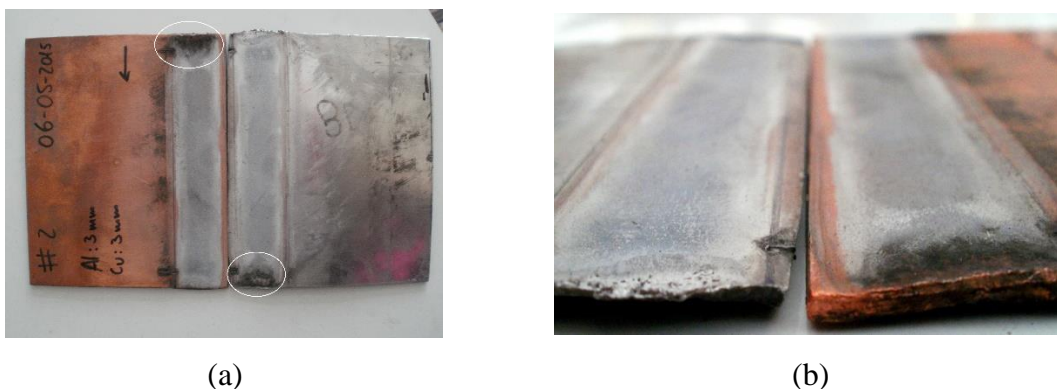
(a) Soldadura UEW1; (b) Detalhe da zona soldada.
